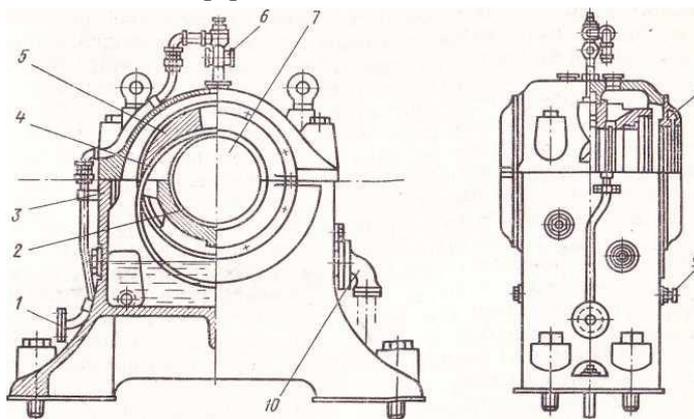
Конструкция подшипника скольжения комбинированной системой подачи масла
